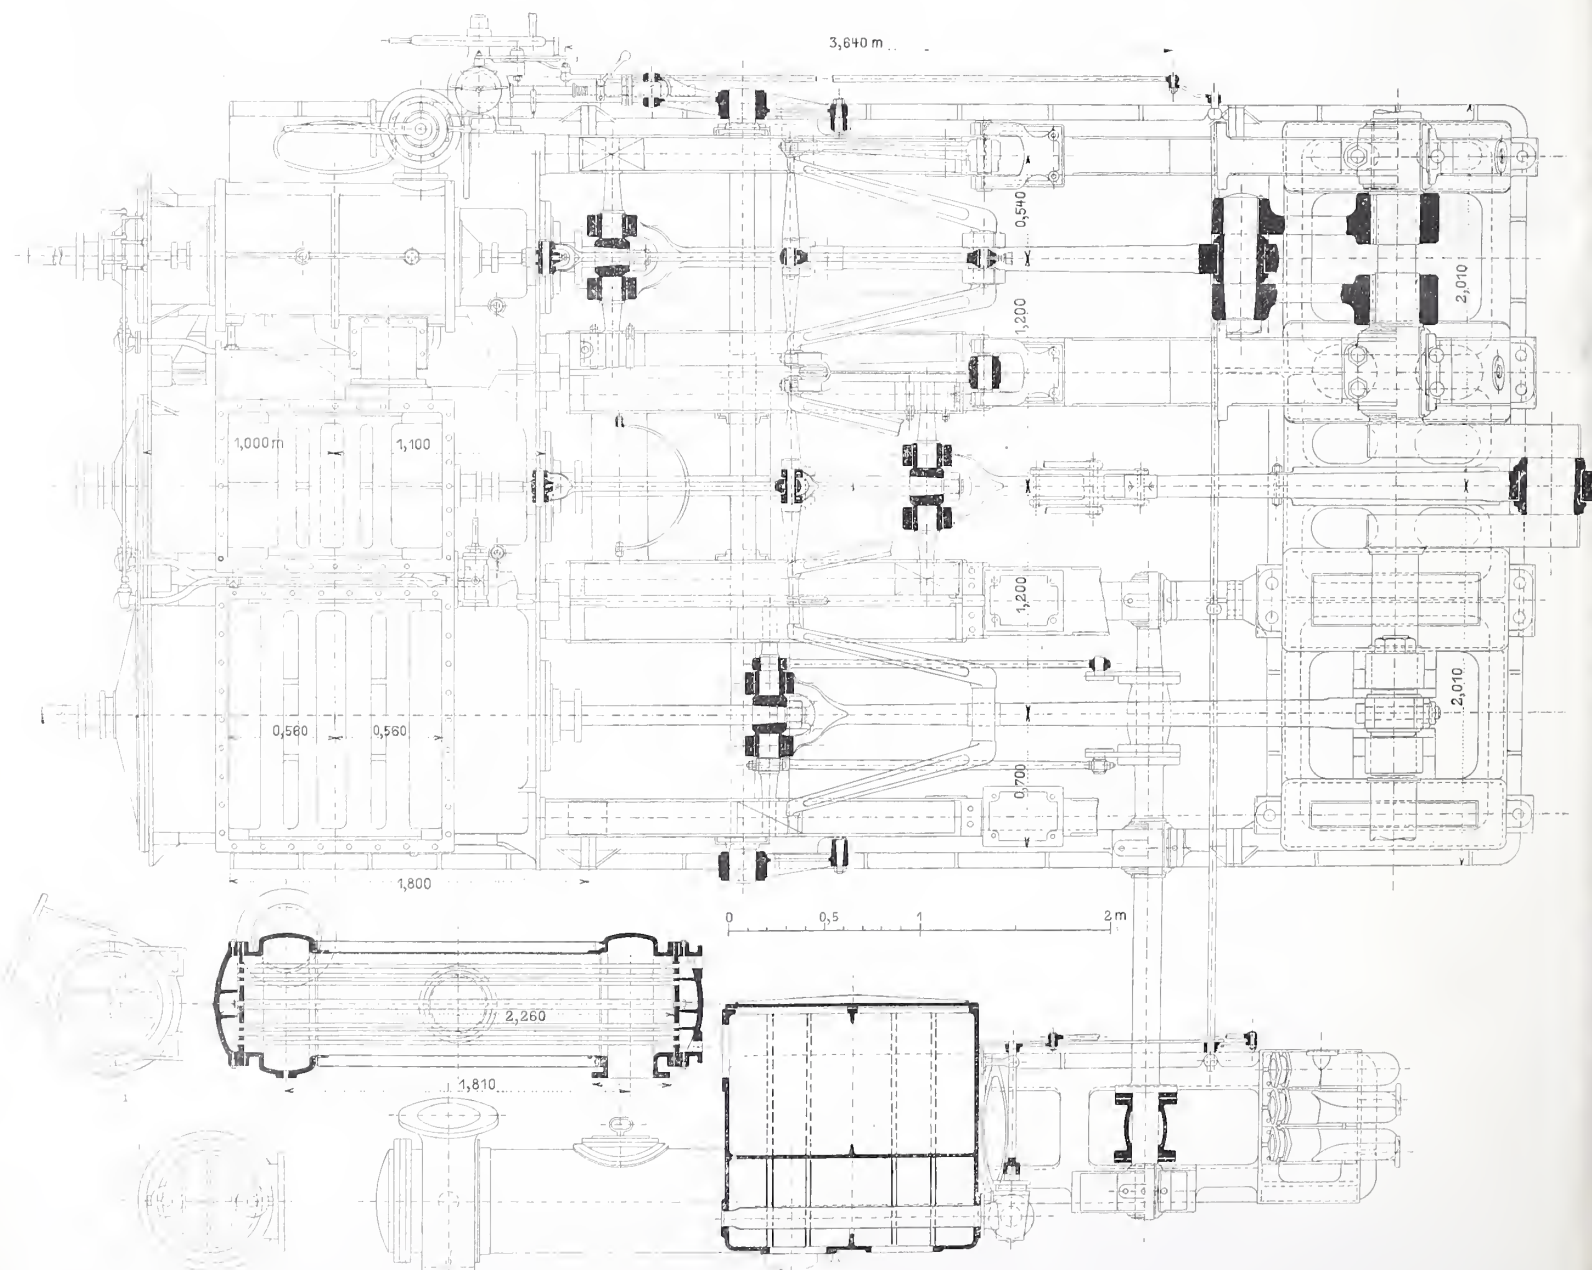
Draufsicht und Schnitt. — Masstab 1:40.
